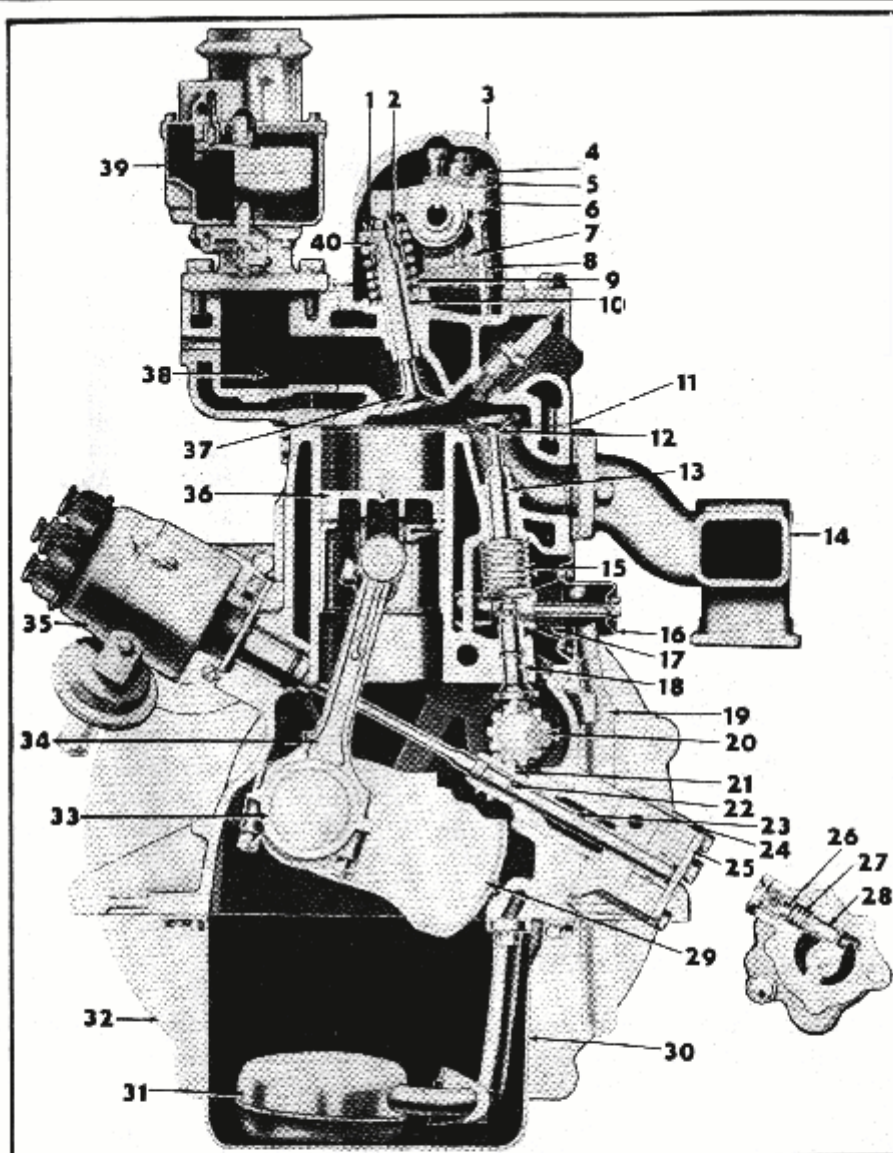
CORTE VERTICAL DO MOTOR, VISTO DE FRENTE
